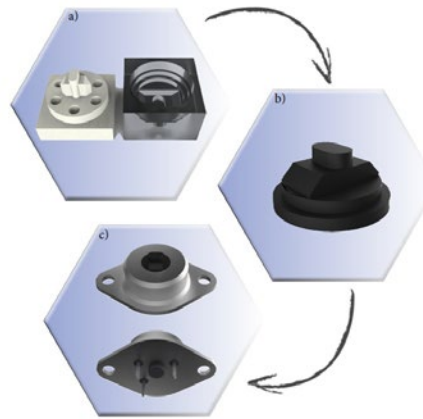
a) Molde para el material encapsulante b) Encapsulado del elemento sensor c) Dispositivo completo con housing diseñado para la aplicación.
